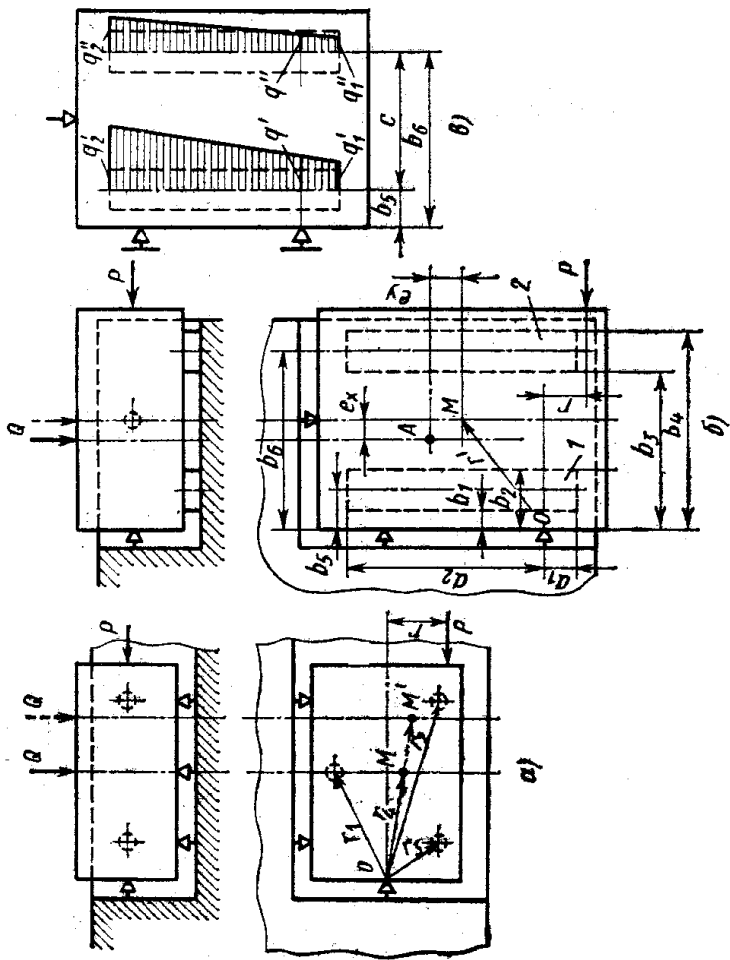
Схемы для расчета сил закрепления заготовок при наличии поворачивающего момента
